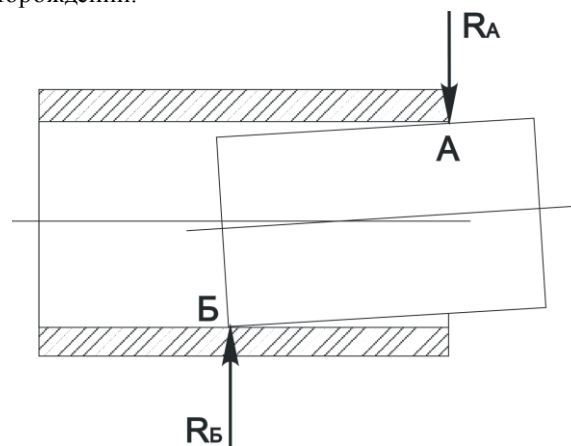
Перекос элементов в поршневых соединениях гидростоек
